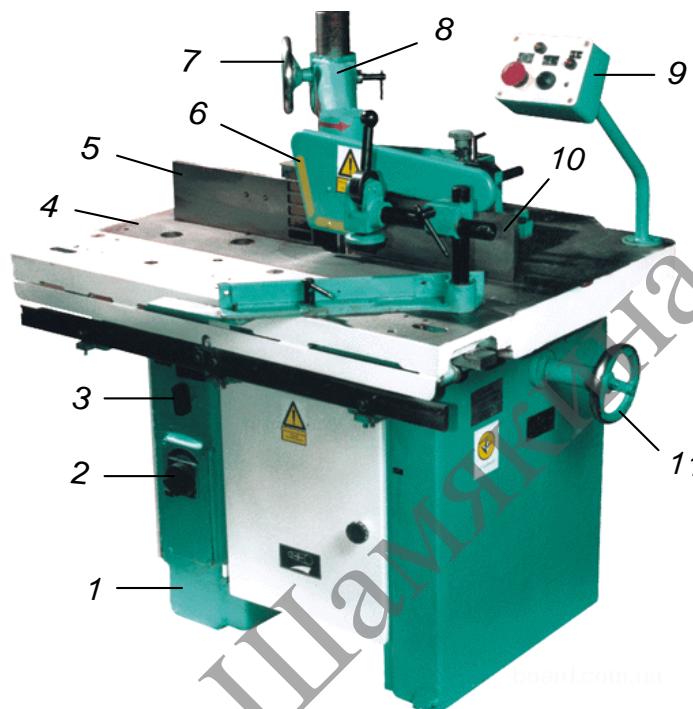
Фрезерный станок ФСШ-1А
